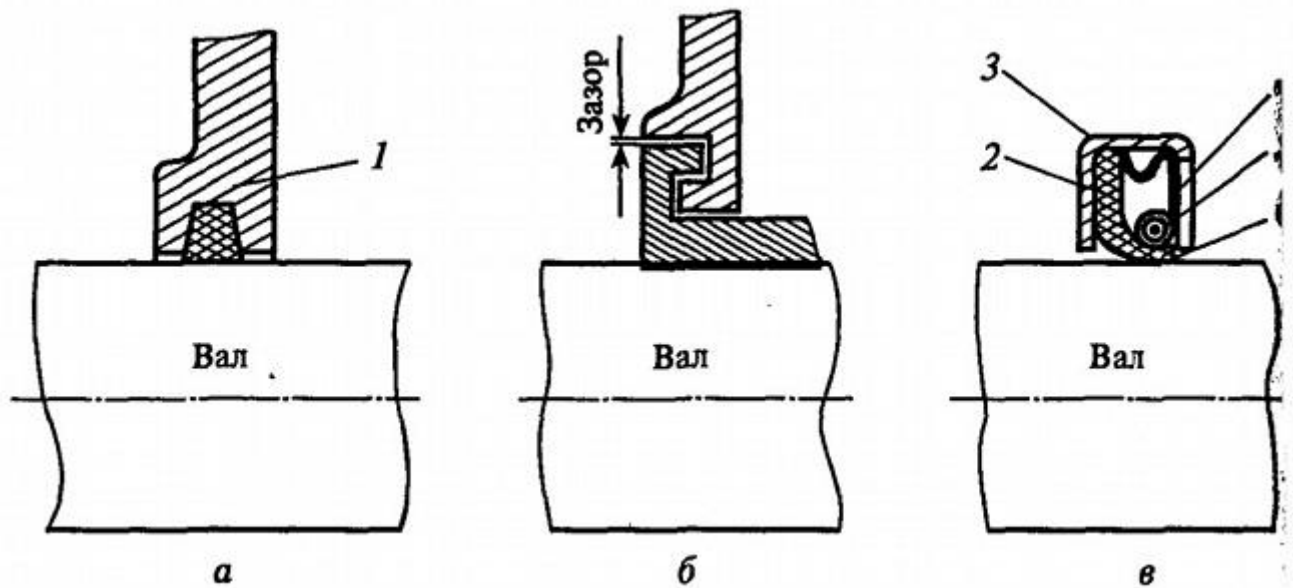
Уплотняющие устройства подшипников качения:
